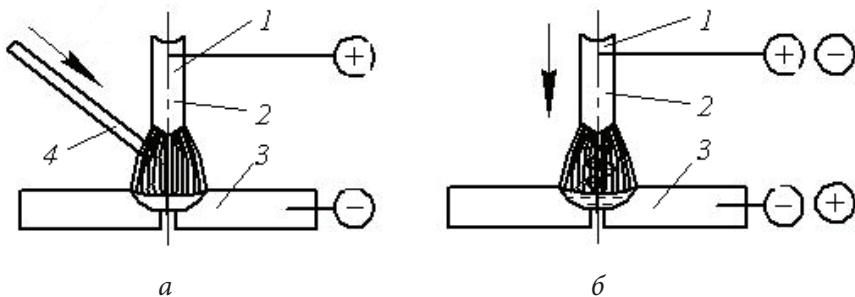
Схемы дуговой сварки: а — сварка неплавящимся электродом; б — сварка плавящимся электродом: (1 — электрод, 2 — электрическая дуга, 3 — свариваемая деталь, 4 — присадочный материал)
